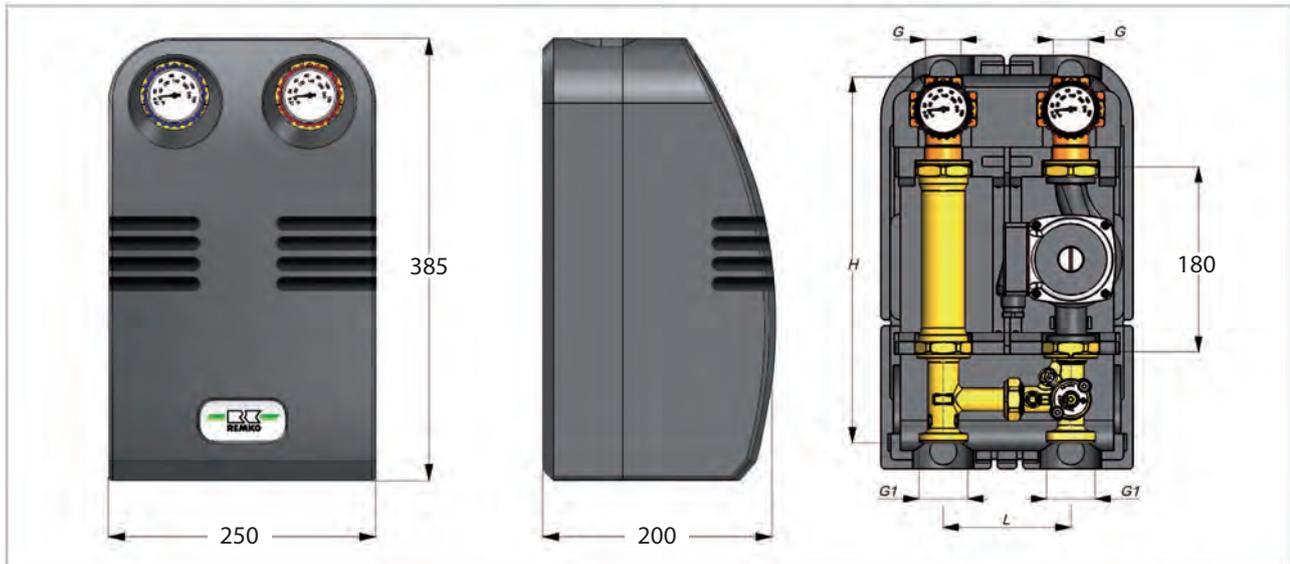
Geräteabmessungen Pumpengruppe HGM
